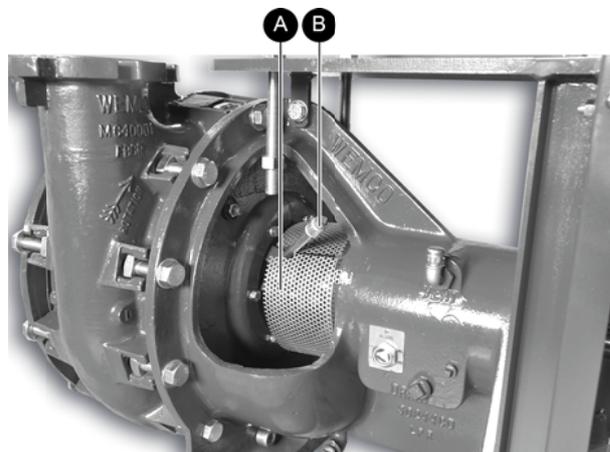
La grille de protection (A) et déposer le tube d'arrosage de tresses (B).
